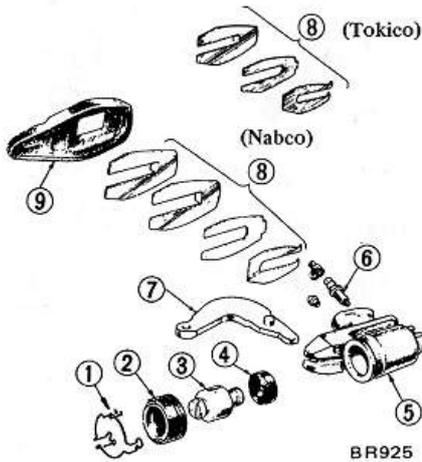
Dépose du cylindre récepteur (modèle à essieu rigide)
